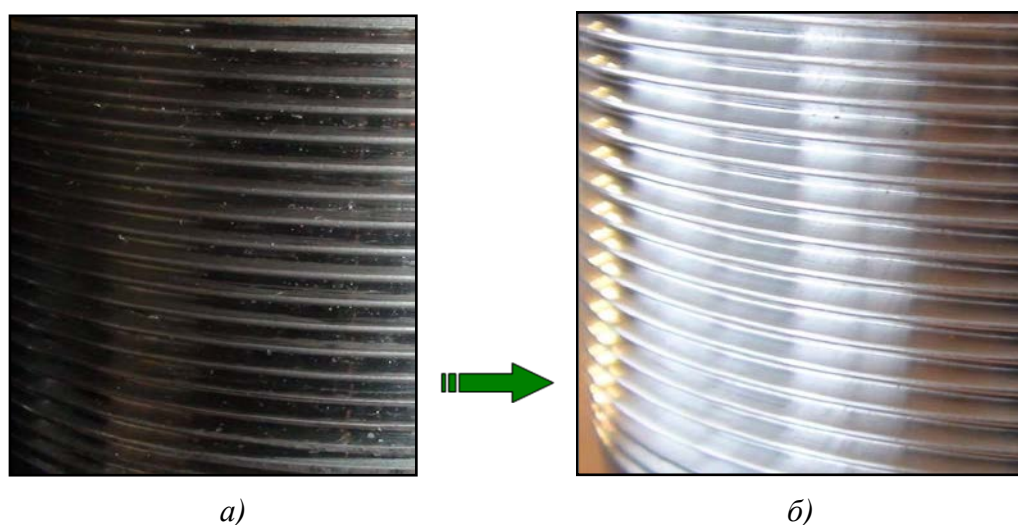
Лазерная очистка поверхности резьб труб, а) внешний вид поверхности резьбы трубы до очистки, б) внешний вид поверхности резьбы трубы после лазерной очистки.
